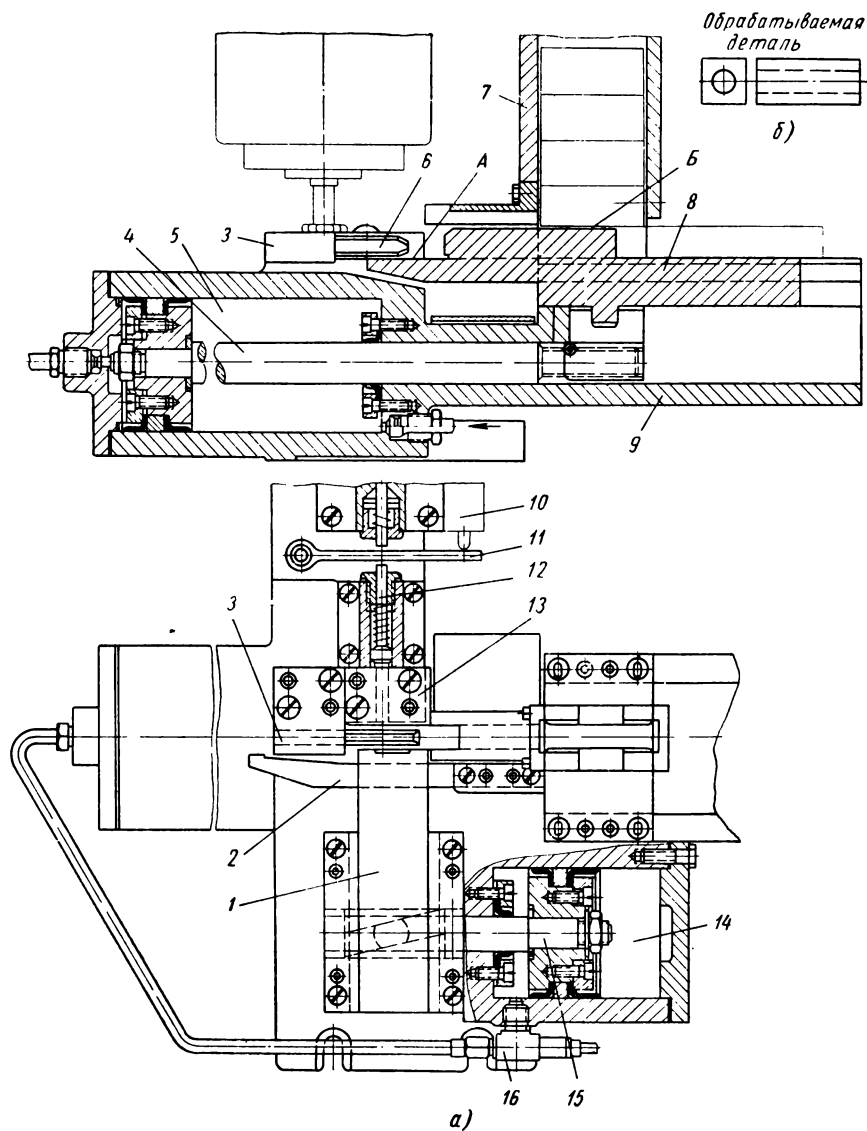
Загрузочное устройство для обработки деталей прямоугольной и круглой формы
